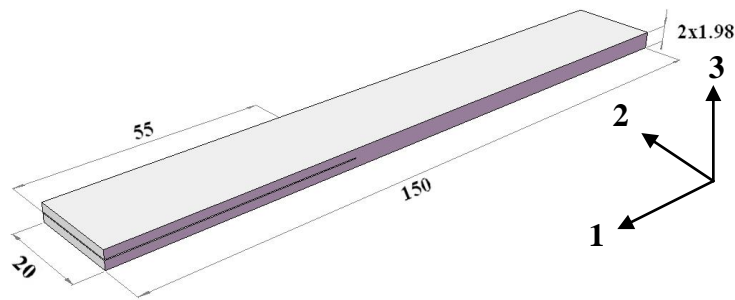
Dimensions des éprouvettes pour la simulation d'un essai DCB
